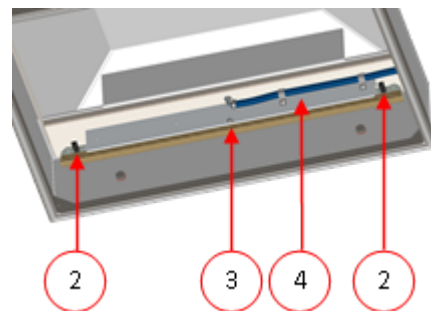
Entfernen der Schweißbleiste (Metalldeckel)
